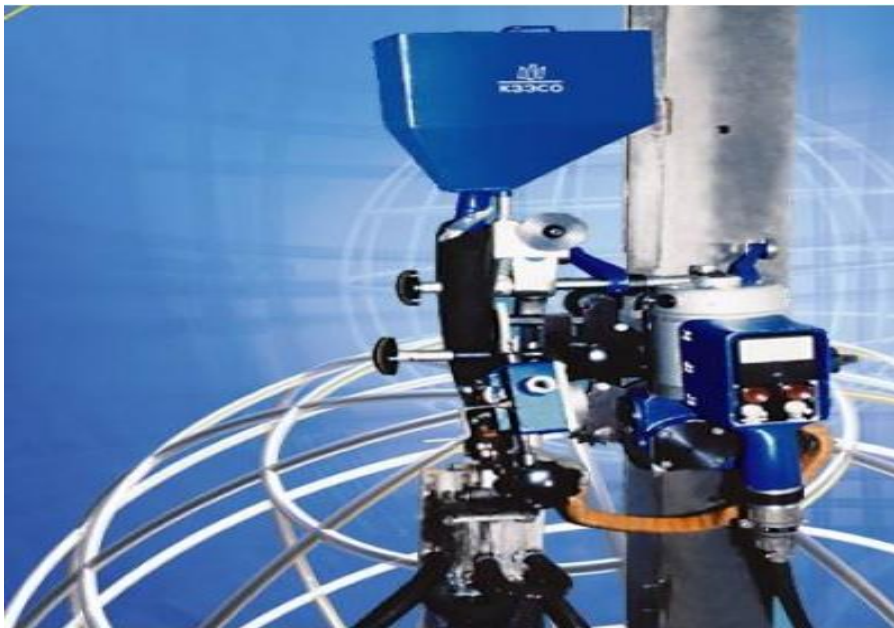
«Сварочный автомат А-820К УХЛ4»[22]
